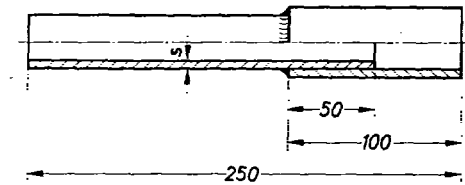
Prüfstück mit Kehlnaht am Überlappstoß für Rohrschweißer an $s = 1,5$ bis 2 mm
